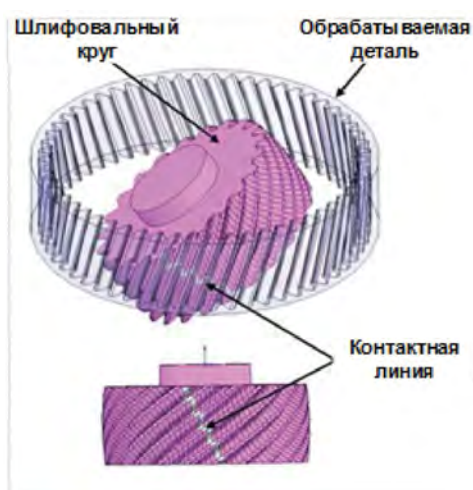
Линия контакта шлифовального червяка и заготовки в 3D-САПР [5]
